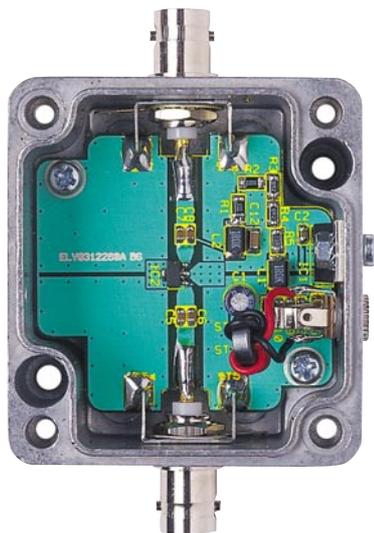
Innenansicht des fertig aufgebauten RFA 403
